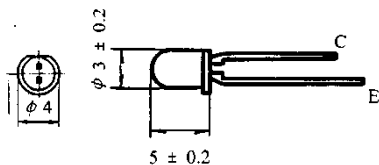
3DU110、120、130 型硅光电三极管外形结构尺寸图
